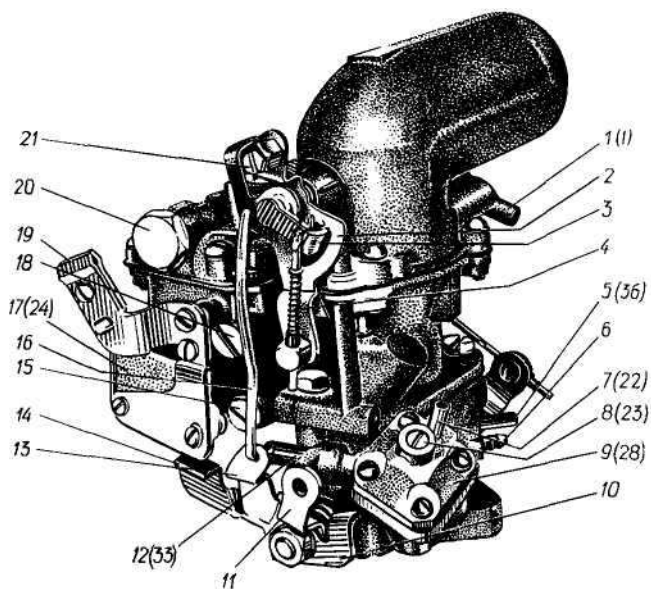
Карбюратор К133; вид спереди (в скобках указаны номера позиций данных деталей на схеме карбюратора (рис. 35)):
